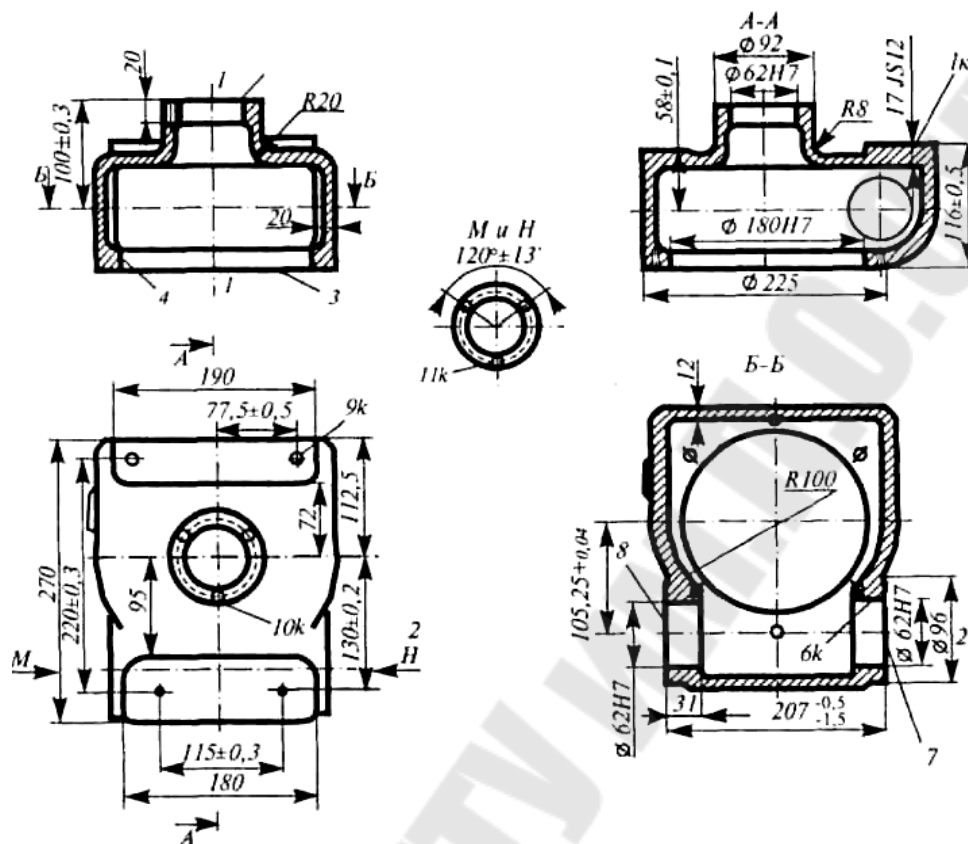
Эскиз корпусной детали с технологической разметкой поверхностей
